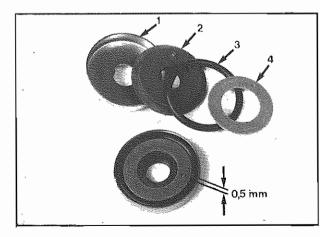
1 - Coperchio parapolvere - Dust cap
